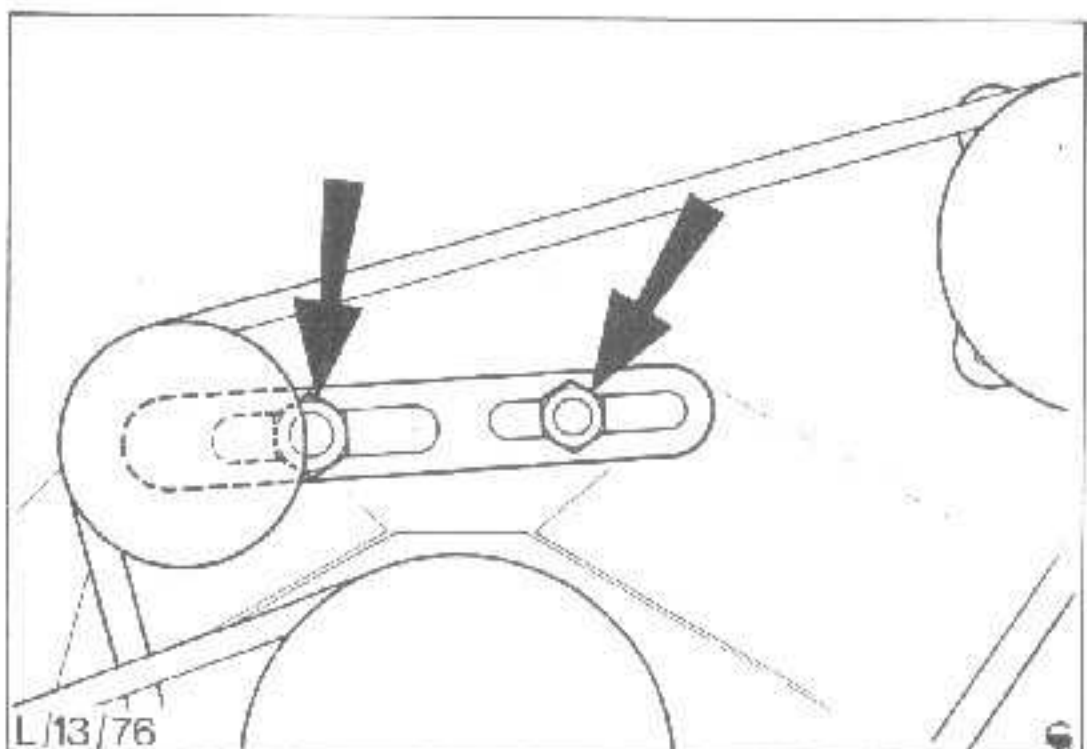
Befestigungsschrauben der Spannrolle (V6-Motor)
